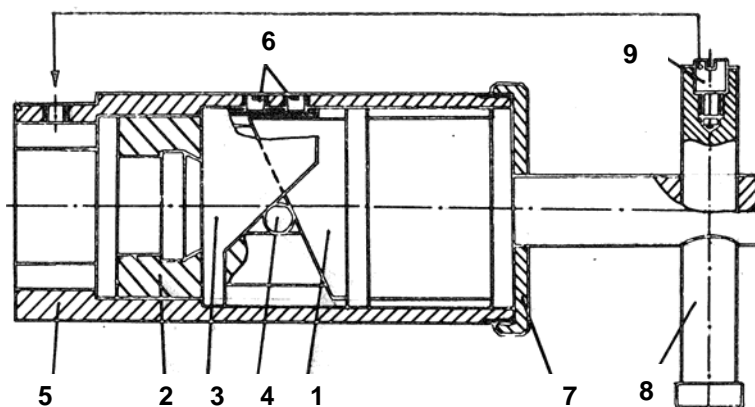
Схема ключа для демонтажа ведущих колес грузовых автомобилей ЗИЛ и ГАЗ
